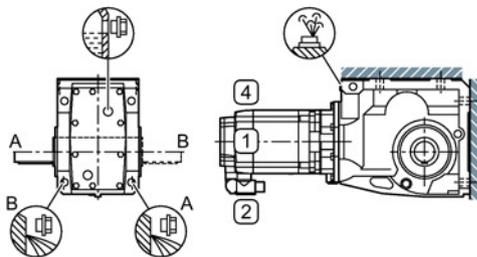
Einbaulagen für Kegelradgetriebe BAD, Aufsteckausführung, Baugröße 39 - 49, 2-stufig
